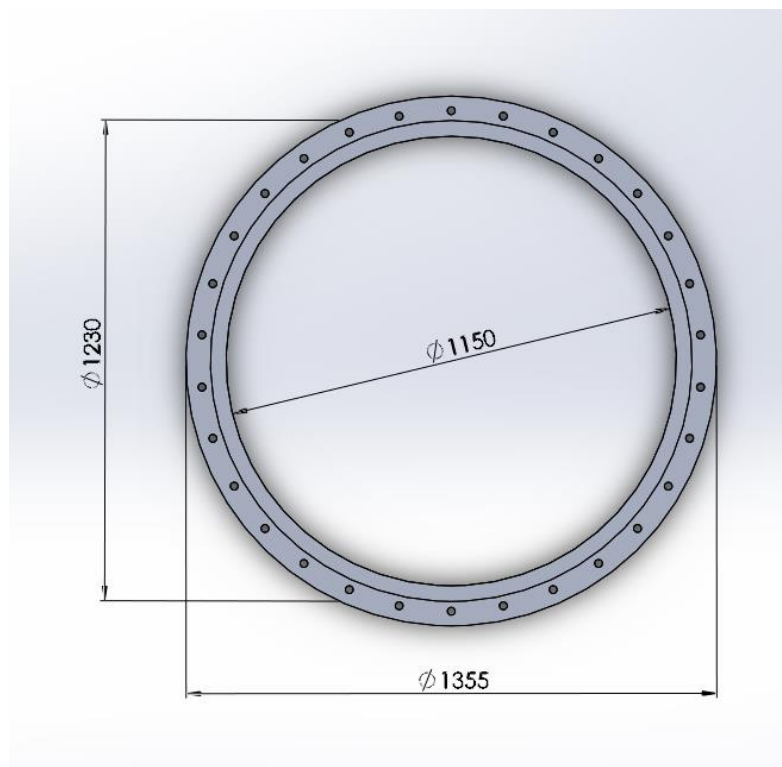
Diámetros de la placa de apoyo del rodamiento.
